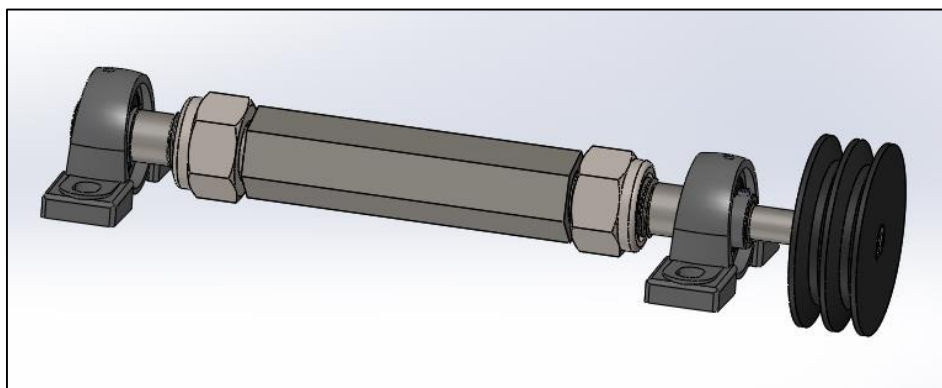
Diseño final del eje principal montado sobre los soportes de rodamientos.
